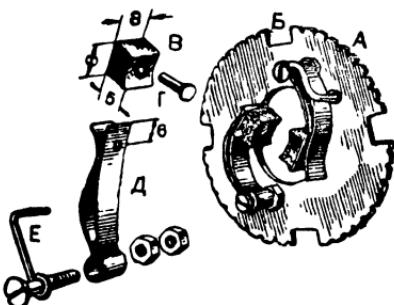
Вариант конструкции щеткодержателя с угольными щетками: А — насечка; Б — вырез для упора; В — щетка; Г — заклепка; Д — пружина; Е — прижим.
